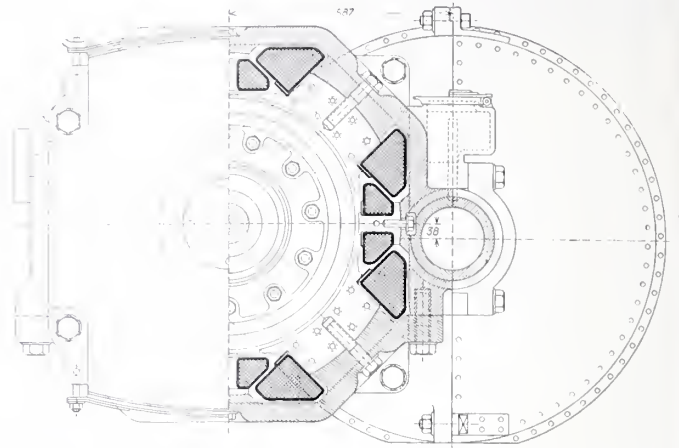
Gleichstromvorgelegemotor der Siemens-Schuckertwerke für Schmalspurbahnlokomotiven. — 1 : 20.
